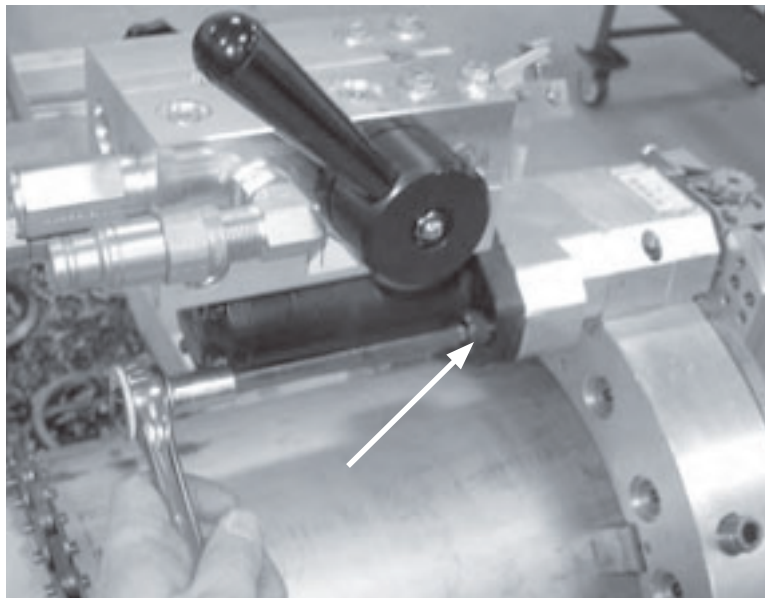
Затяните 2 шт. винтов, соединяющих двигатель с переходником.
